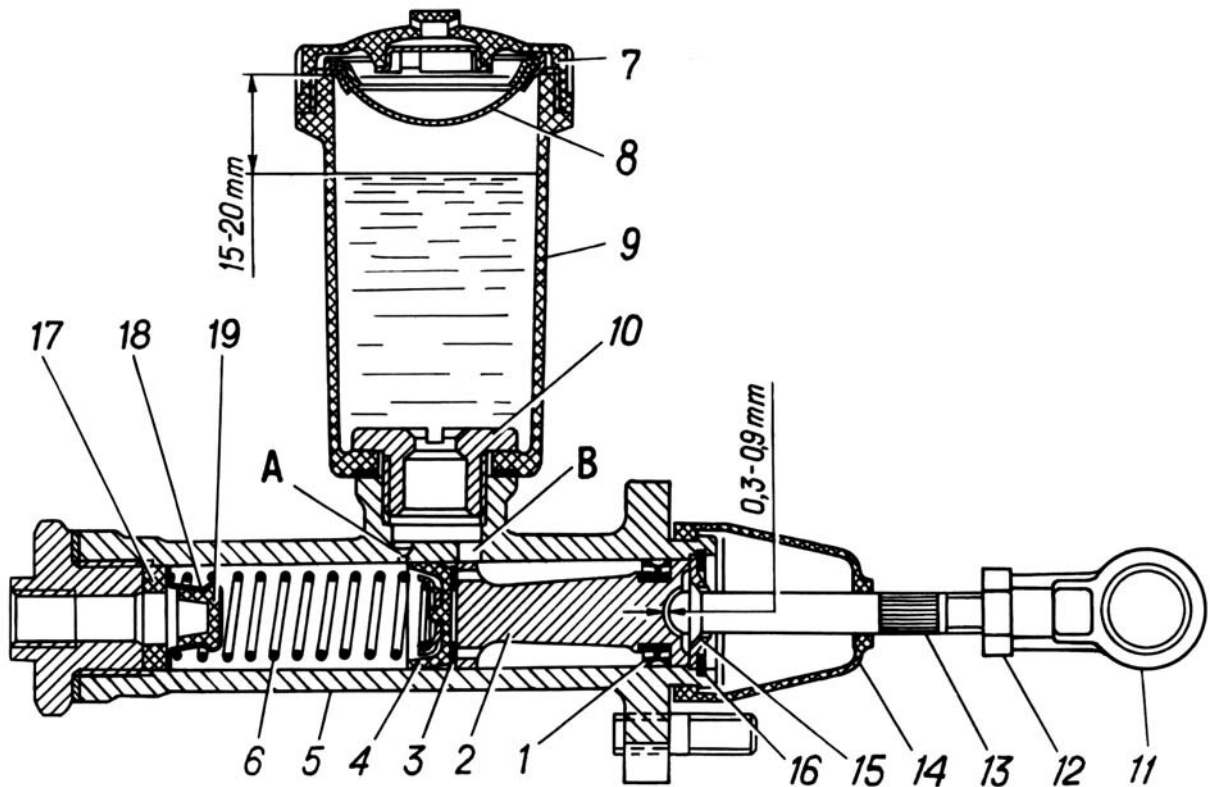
Главный цилиндр привода выключения сцепления: А - компенсационное отверстие; В - перепускное отверстие; 1 и 4 - манжеты; 2 - поршень; 3 - пластинка; 5 - корпус главного цилиндра; 6 - пружина; 7 - крышка; 8 - отражатель; 9 - наполнительный бачок; 10 - штуцер; 11 - проушина; 12 - контргайка; 13 - толкатель поршня главного цилиндра; 14 - чехол; 15 - упорная шайба; 16 - стопорное кольцо; 17 - кольцо упорное; 18 - обойма клапана; 19 - клапан
